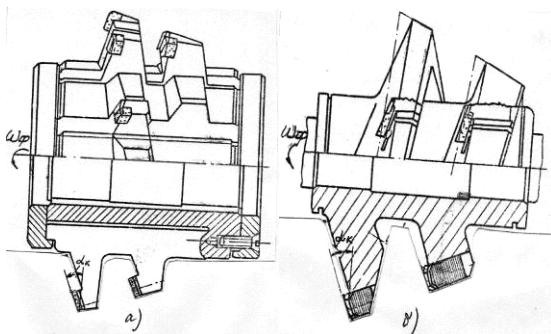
Конструкция специальных твердосплавных фрез
